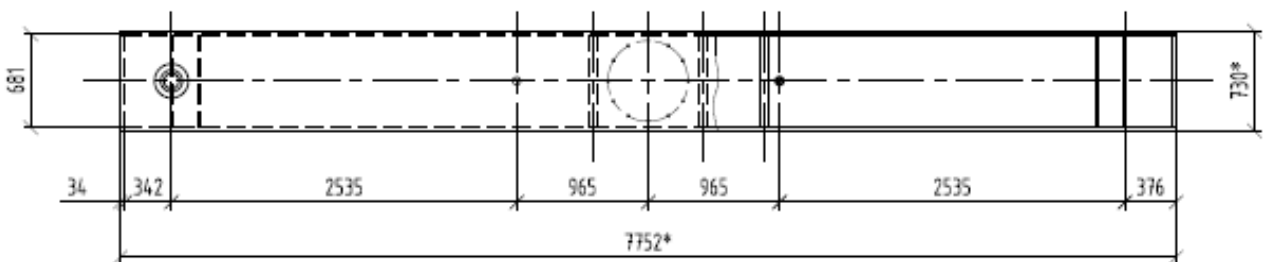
Верхня балка гойдальної опори (вид зверху)
